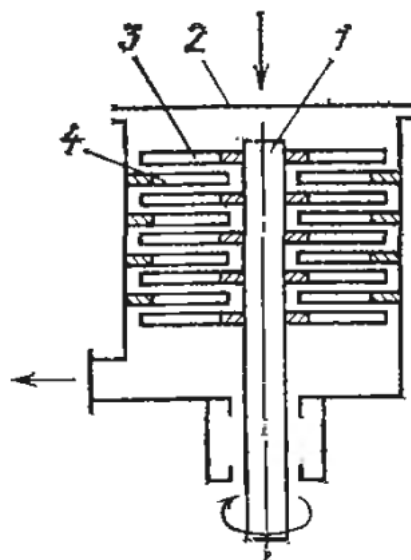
Конструктивная схема турбомолекулярного насоса: 1-ротор, 2-корпус, 3-рабочие колеса, 4-неподвижные статорные диски
